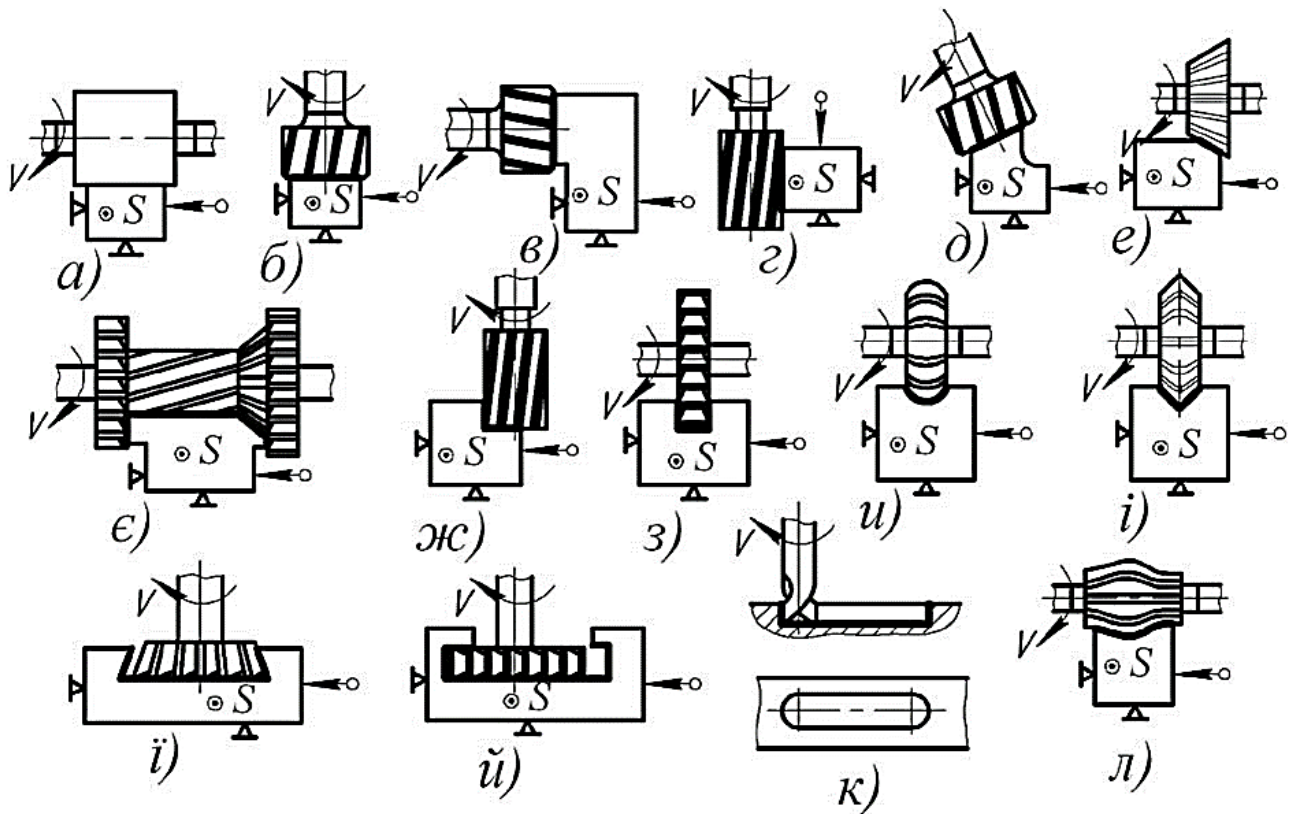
Схеми обробки заготовок на горизонтально- і вертикально-фрезерних верстатах
